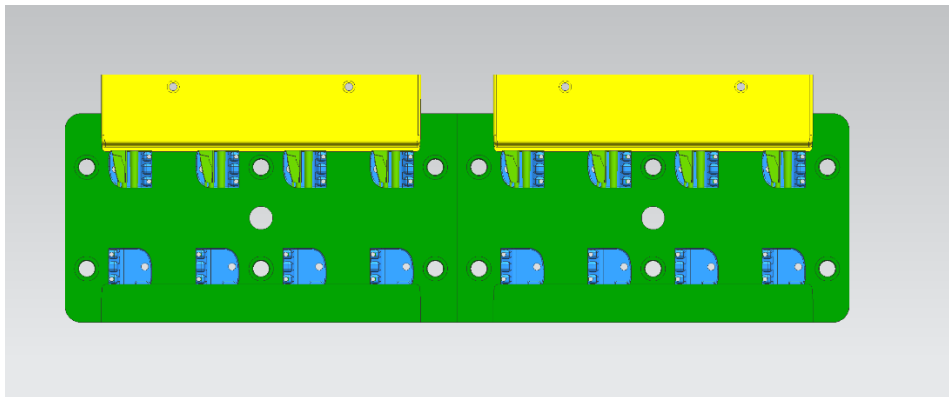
Disposición de cavidades en postizos, vista en planta
